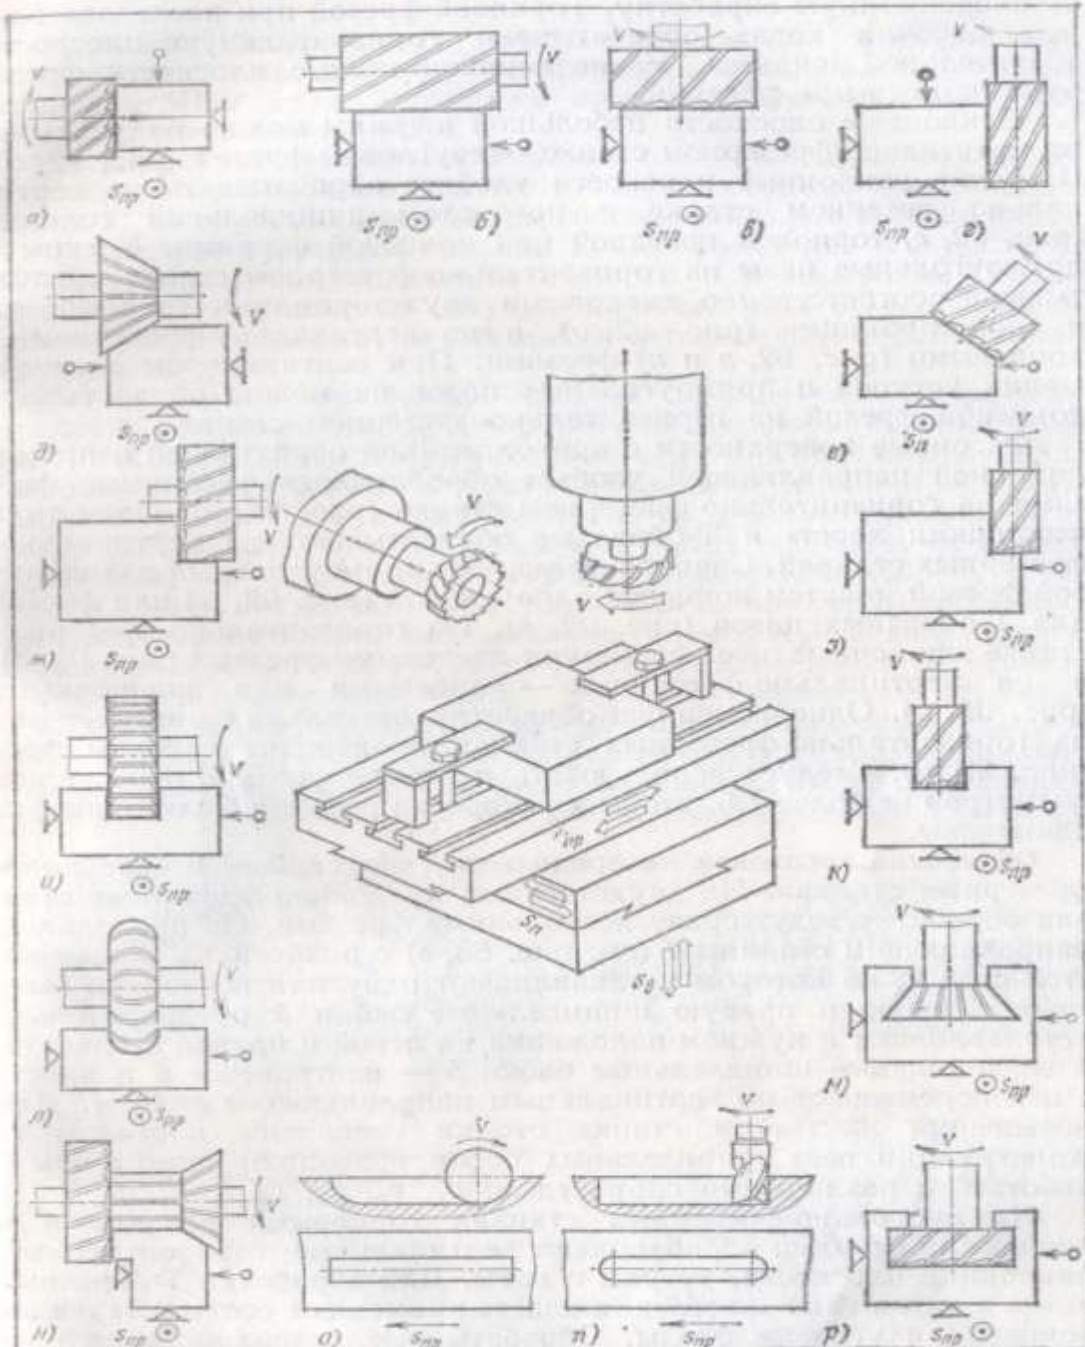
Схемы обработки поверхностей на универсальных фрезерных станках
